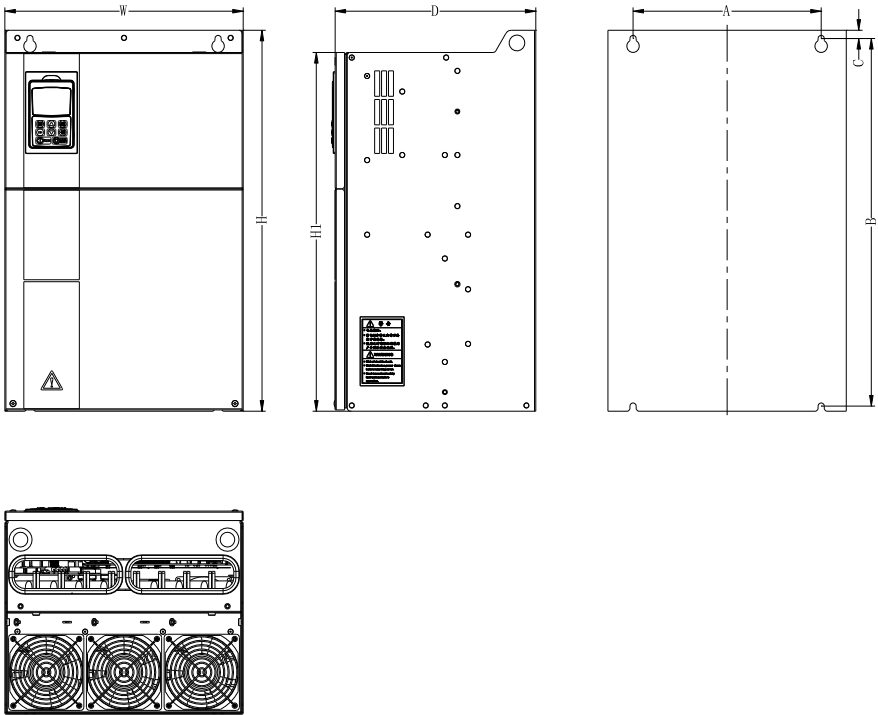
11 ~ 132kW 外型尺寸及安装尺寸示意图
